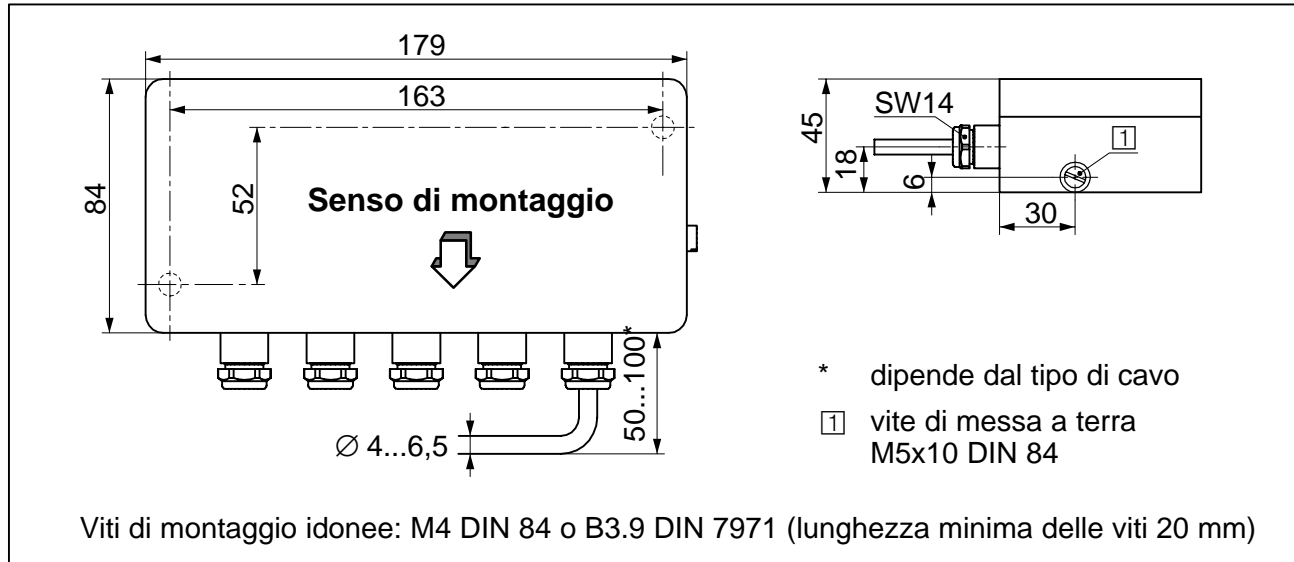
Dimensioni di montaggio della VKK1-4
